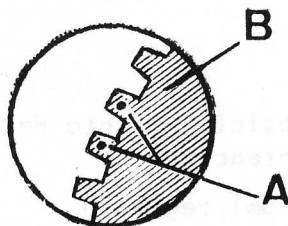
Marcas del engranaje del árbol de levas para montar el de la bomba inyectora
